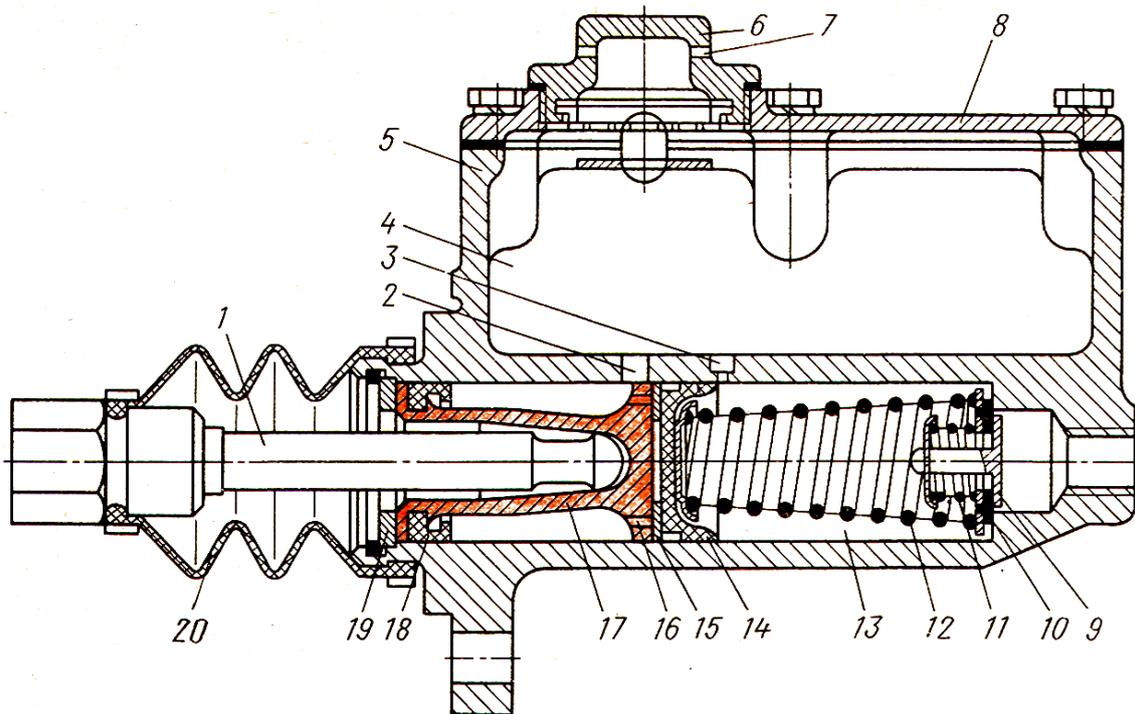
Главный тормозной цилиндр ГАЗ-53а: 1 – головка толкателя; 2 – перепускное отверстие; 3 – компенсационное отверстие; 4 – полость; 5 – корпус; 6 – резьбовая пробка; 7 – отверстия; 8 – крышка; 9 – перепускной клапан; 10 – обратный клапан; 11 – пружина; 12 – возвратная пружина; 13 – цилиндр; 14 – резиновая манжета; 15 – кольцеобразный клапан; 16 – отверстия; 17 – поршень; 18 – уплотнительное кольцо; 19 – упорная шайба; 20 – чехол.
